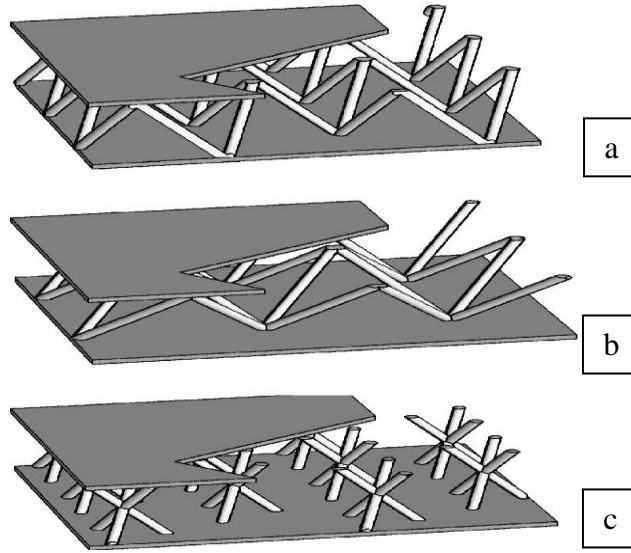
Birim hücre çekirdek yapıları a) oluklu prizmatik çekirdek, b) elmas oluklu çekirdek, c) kesik prizmatik çekirdek
